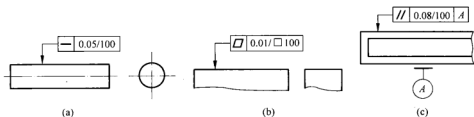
被测要素局部范围内公差带要求的标注示例
